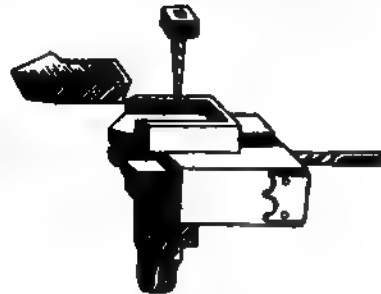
Stahlhalter einer Drehbank mit Schlittenführung, um 1480.
